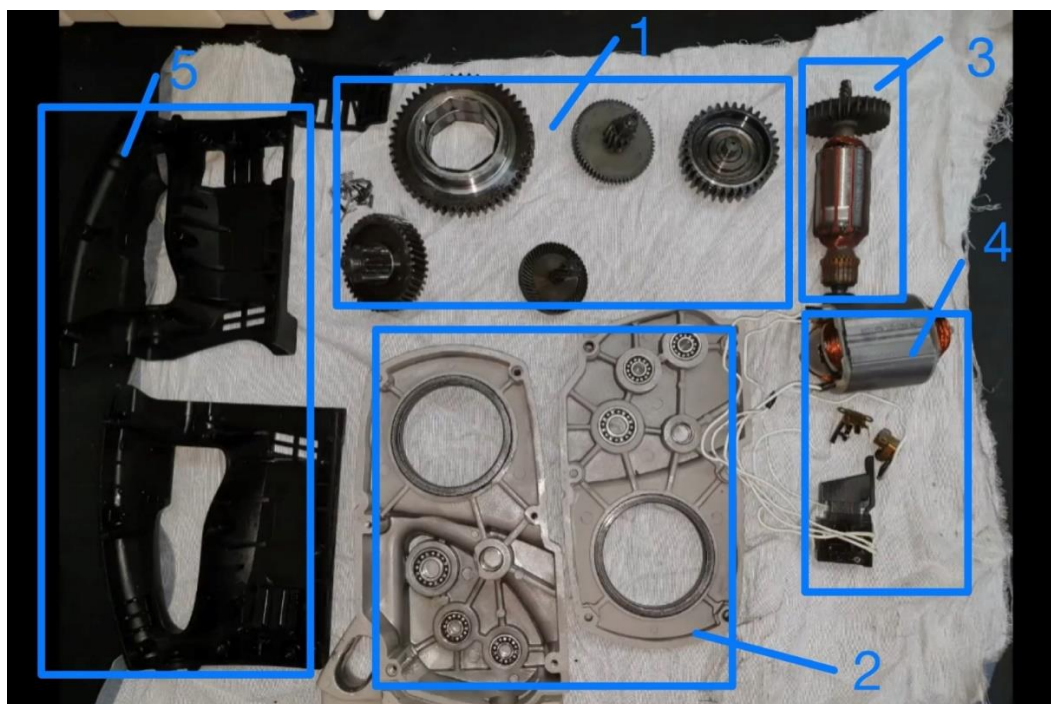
Состав электрический клупп : 1- передаточные колеса; 2- корпус резьбонарезной насадки и подшипники; 3- якорь; 4- двигатель и кнопка включения; 5- корпус двигателя и рукоятка
